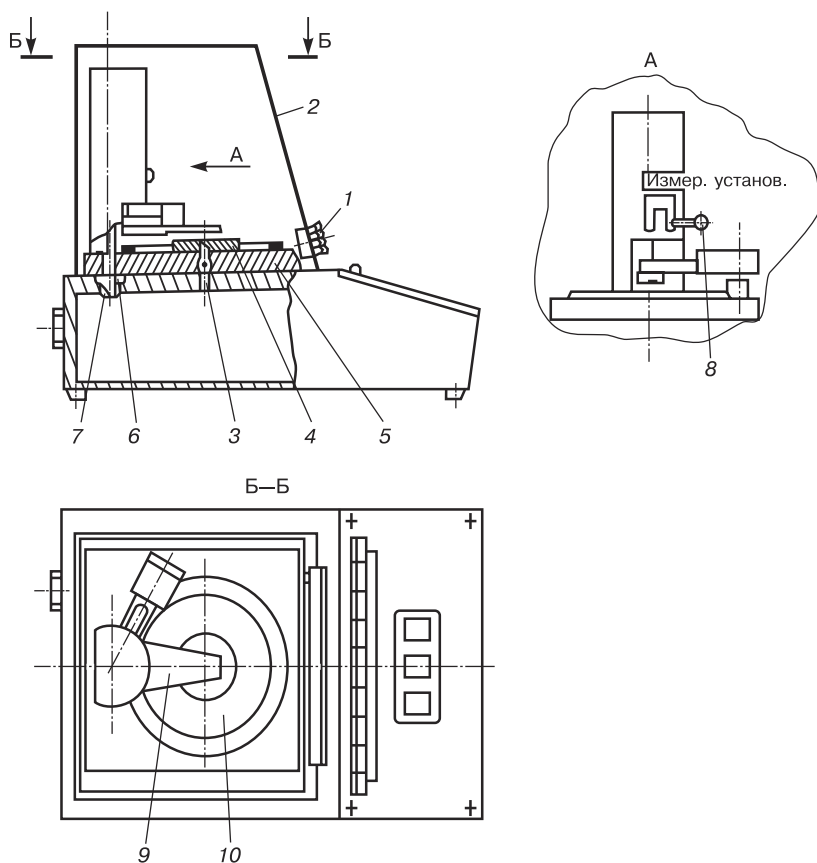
Схематическое изображение контактного устройства: 1, 3 — винты; 2 — кожух; 4 — столик; 5 — плита; 6 — гайка; 7 — стержень; 8 — рукоятка; 9 — пластина; 10 — кольцо
